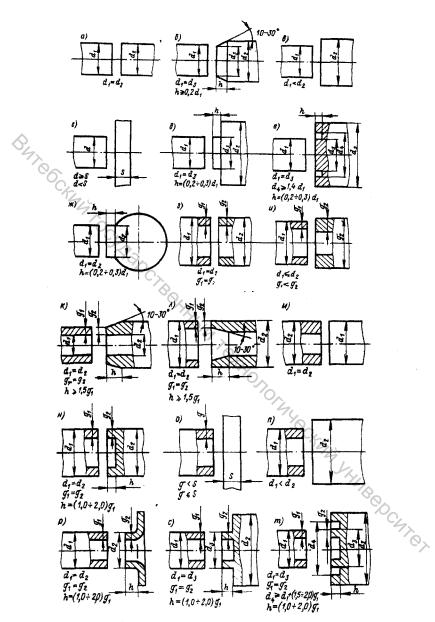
Основные формы заготовок под сварку трением
